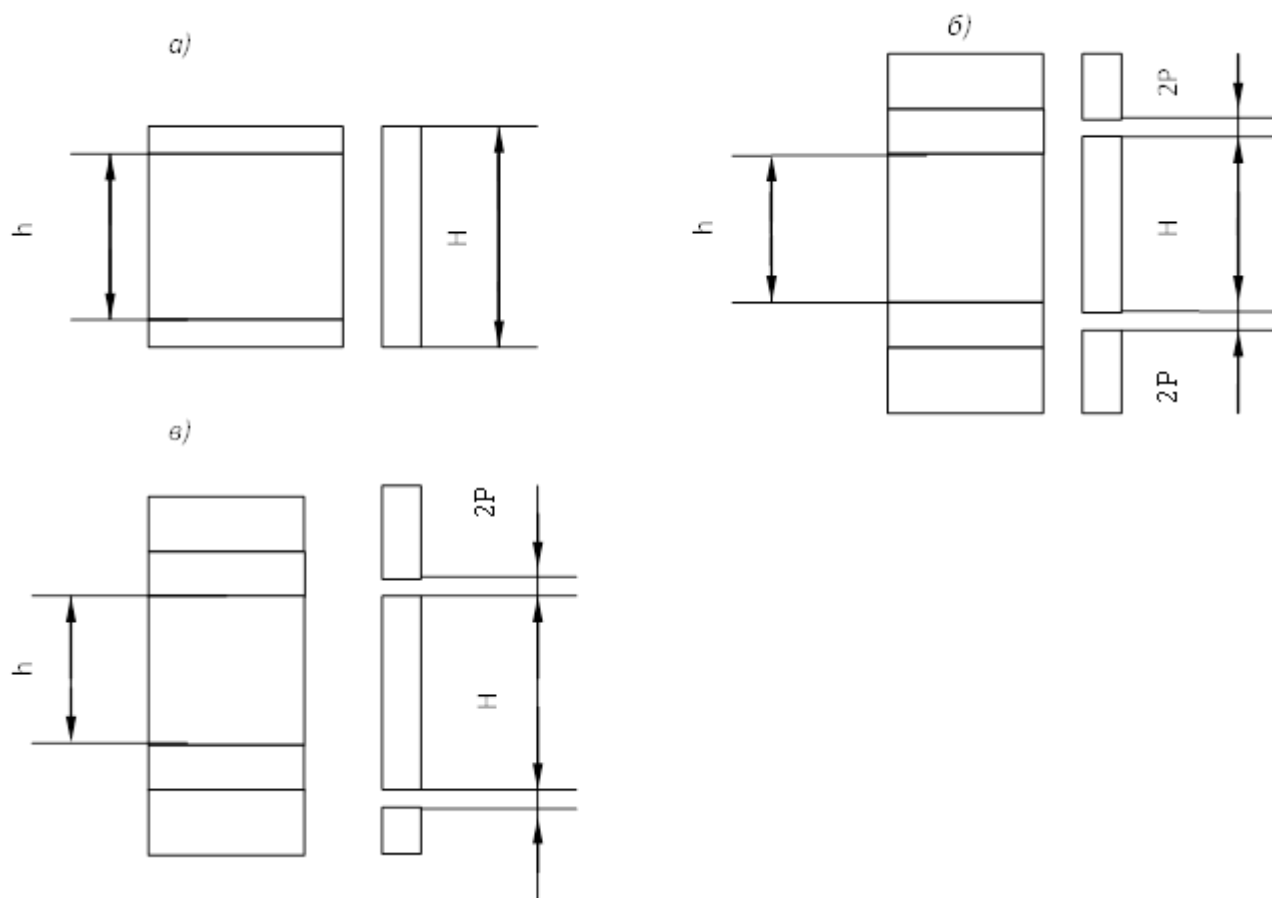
Схемы формирования проемов корпусов по высоте: а – однодверный корпус; б – в – трехдверный корпус
